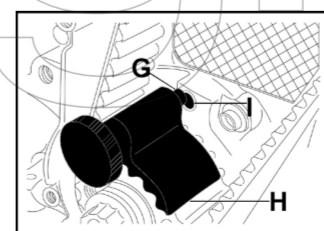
Montar la plantilla del cigüeñal insertando el perno G de la herramienta H en el orificio I.
